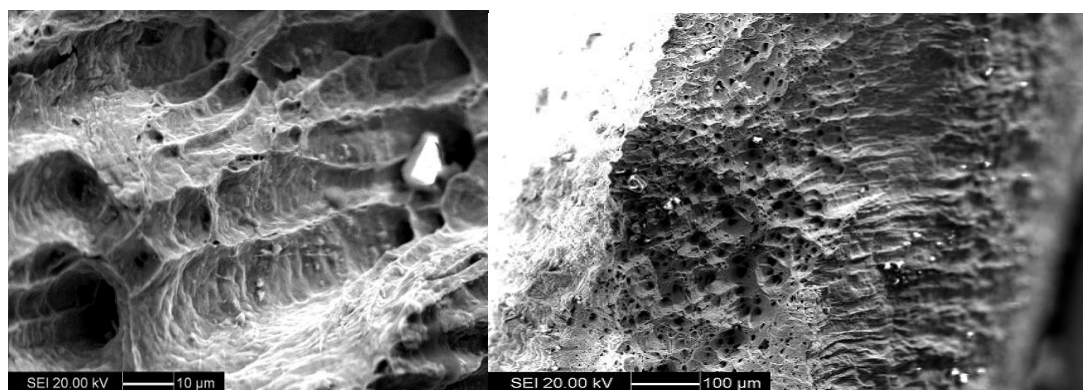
Superfície da fratura do corpo de prova 15. Estrias podem ser observadas.
